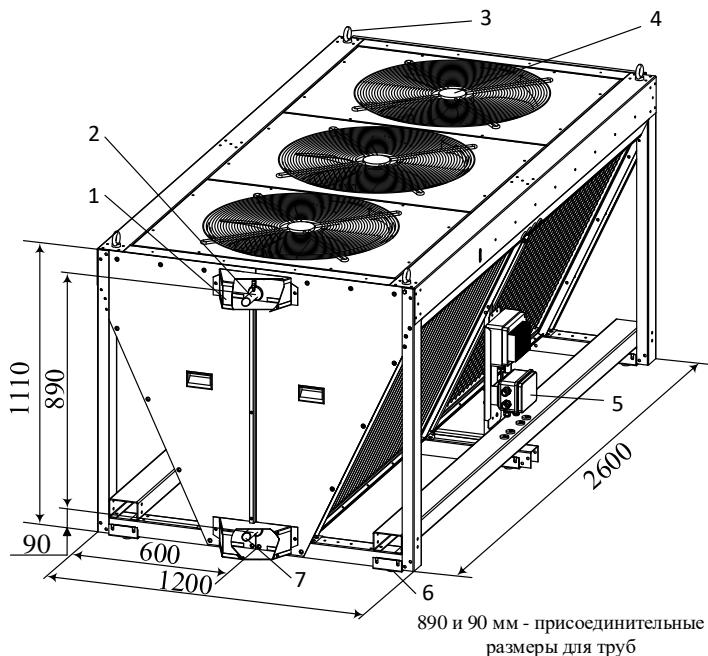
Компоновка и основные размеры конденсаторов 128 и 145
